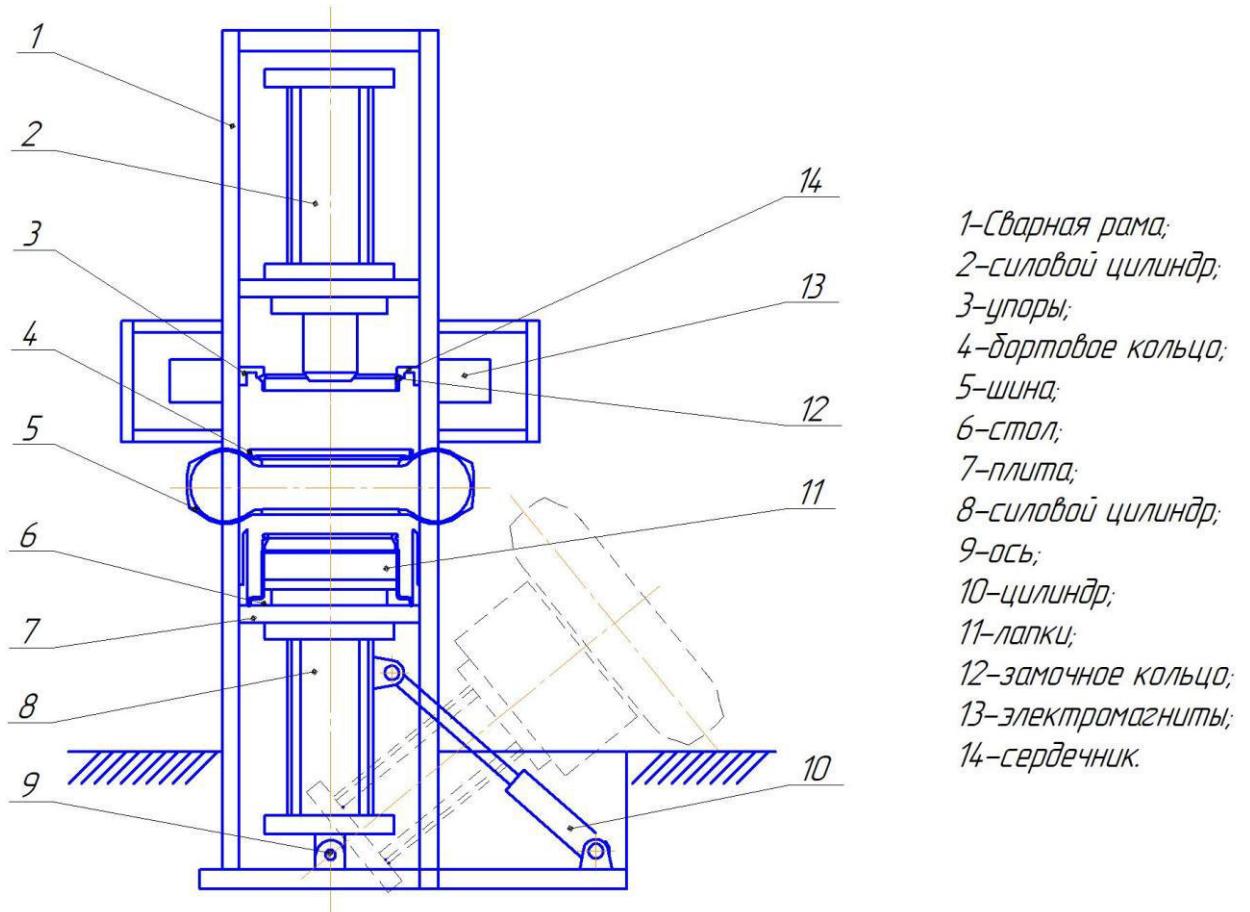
Стенд для демонтажа шин колес грузовых автомобилей
